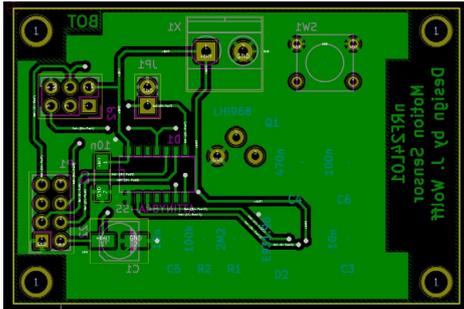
PCB del sensor de movimiento nRF24 - parte inferior
